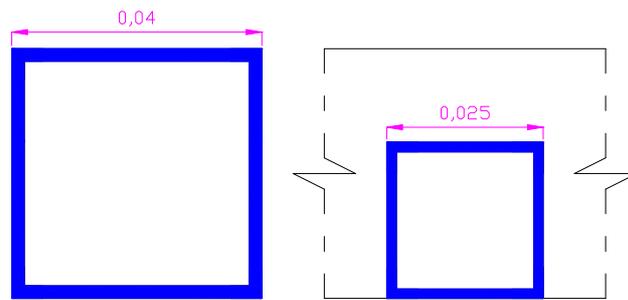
Suelda vista frontal (Izquierda: Perimetral; Derecha: Travesaño).
